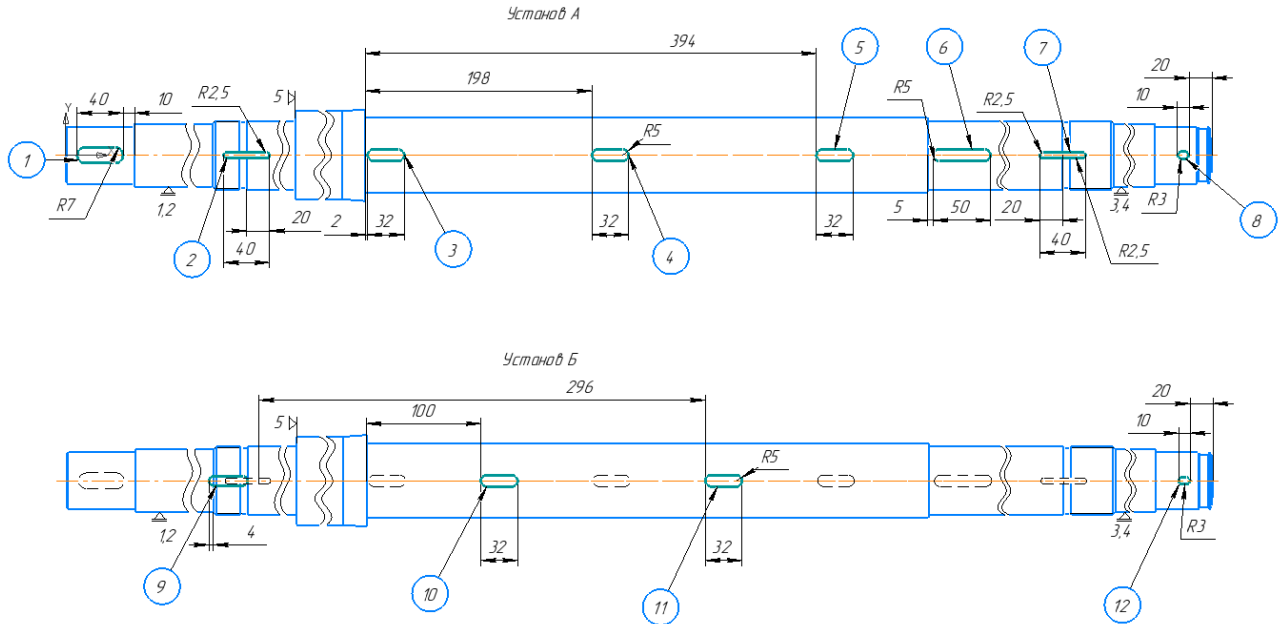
Ескіз обробки для операції 055 Горизонтально-Фрезерна з ЧПК
